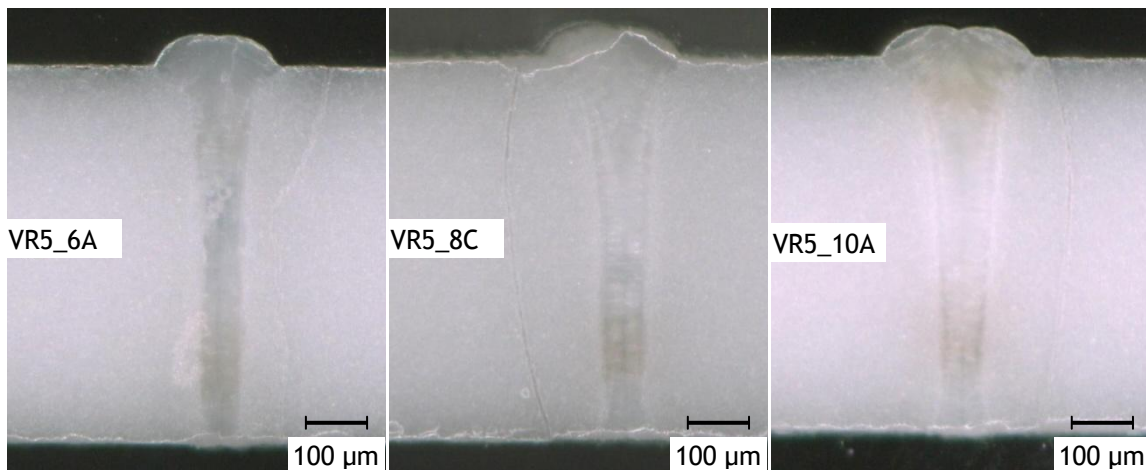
Beispiele für teilweise günstige Blindschweißungen aus VR5
